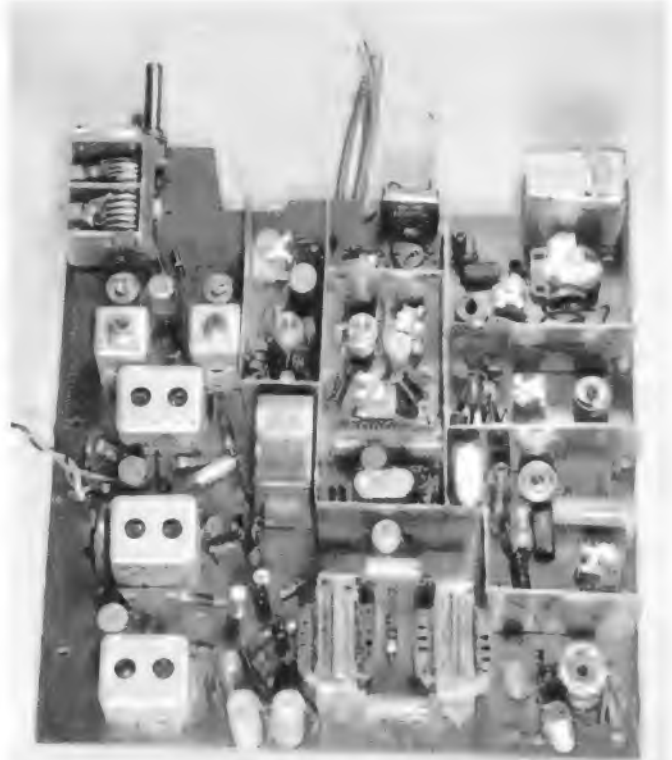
Fertig bestückte Platine mit der Lage der Abschirmmände. Der Drehkondensator ist mit einem Winkel auf die Platte geschraubt
